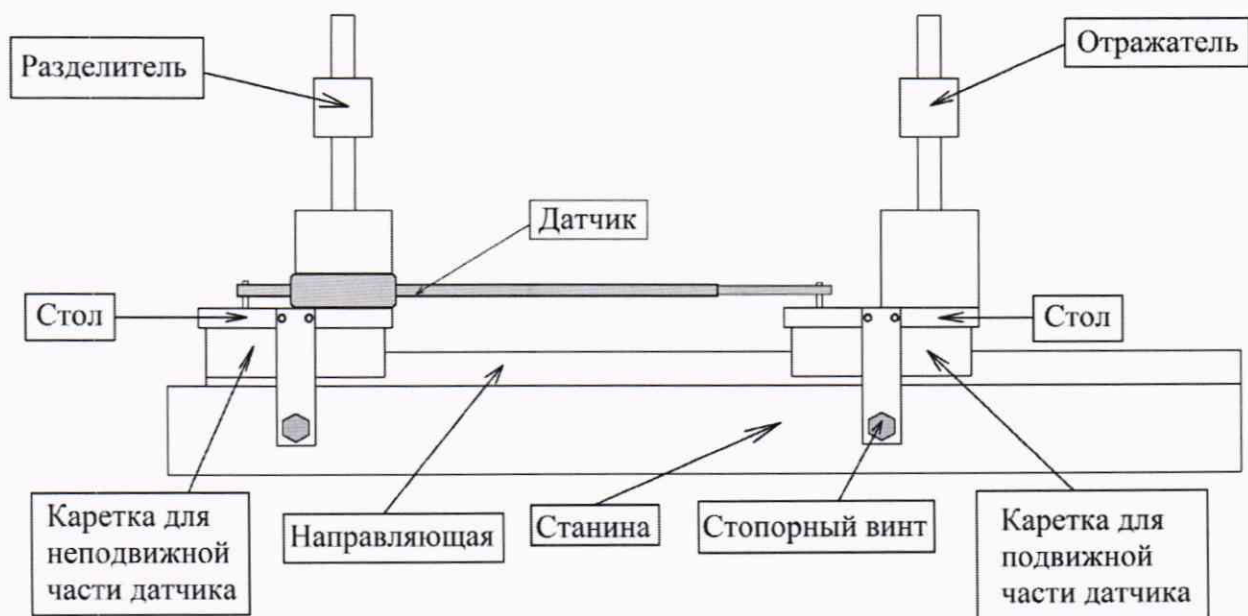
Внешний вид приспособления для крепления преобразователей и датчиков линейных перемещений
